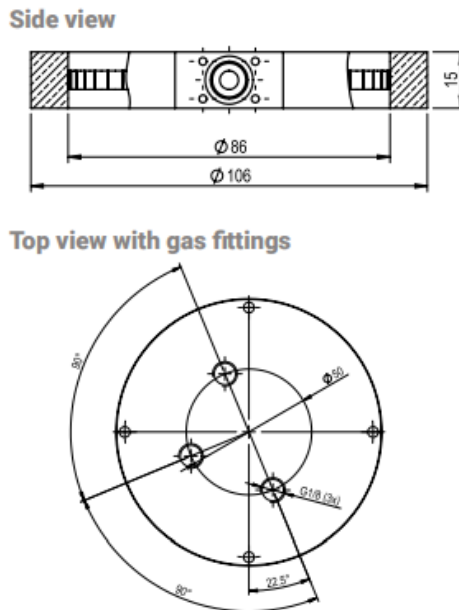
Dimensiones de la celda multipaso IRcell-4m
